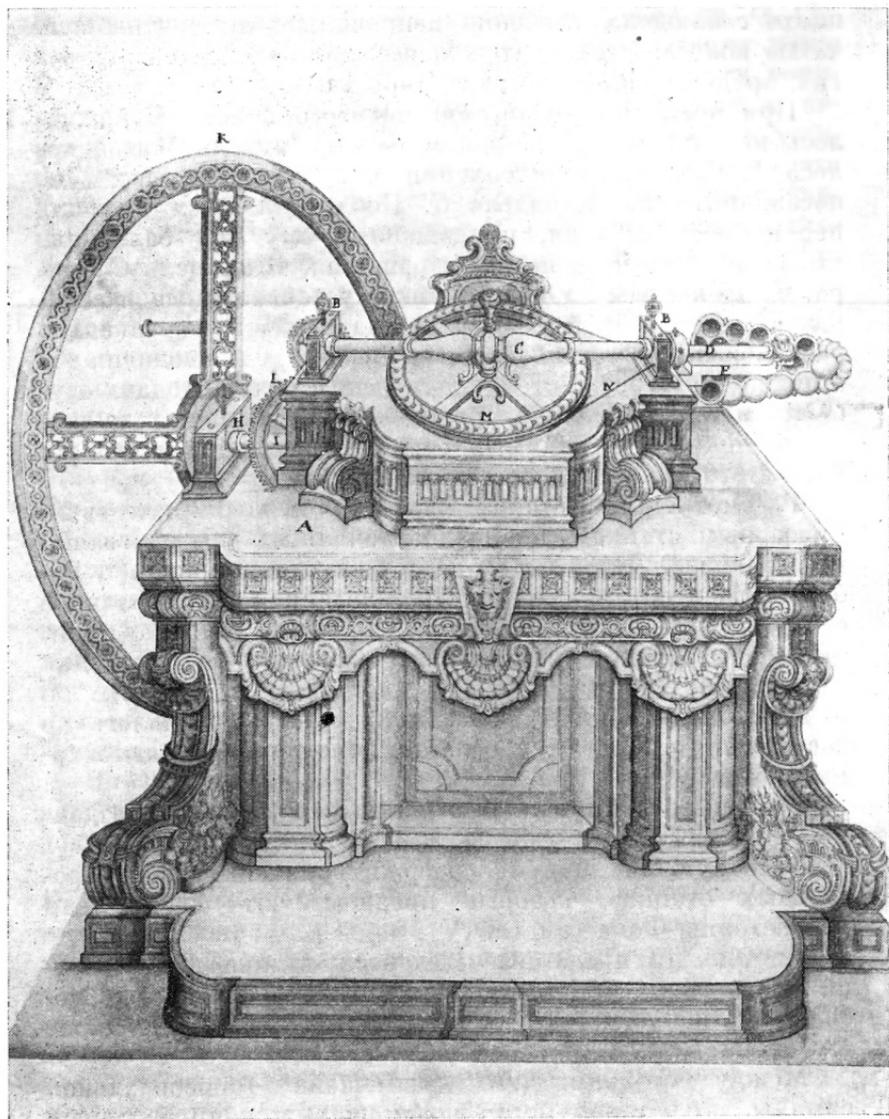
Станок для фрезерования грибовидной фрезой («Театрум ма-
